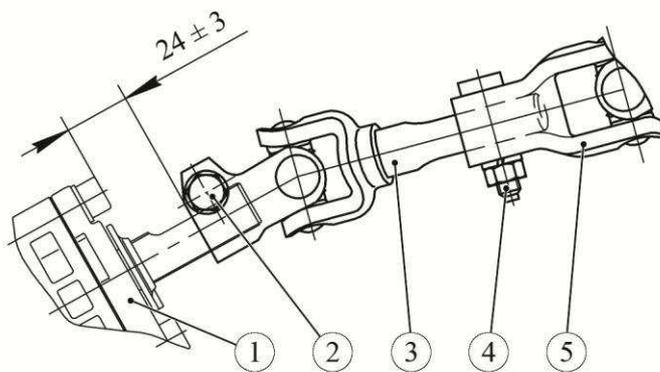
Установка рулевого вала на вал шестерни рулевого механизма:
